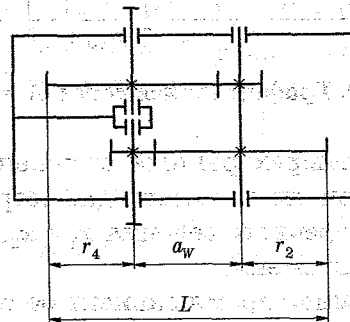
Соосный двухступенчатый цилиндрический зубчатый редуктор
